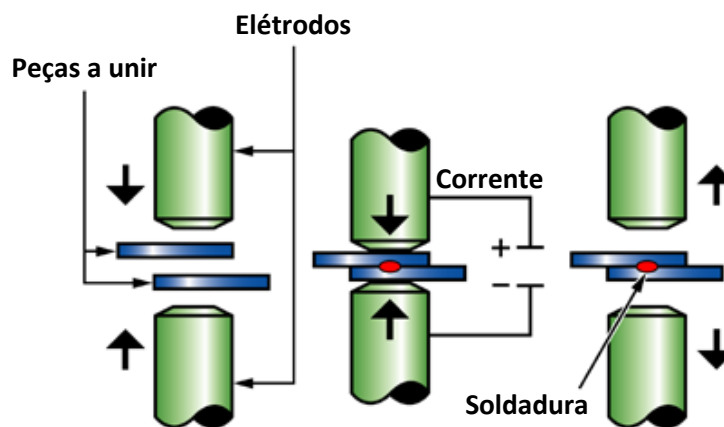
Representação Simplificada do Processo de Soldadura por Pontos (adaptado de [28]).
